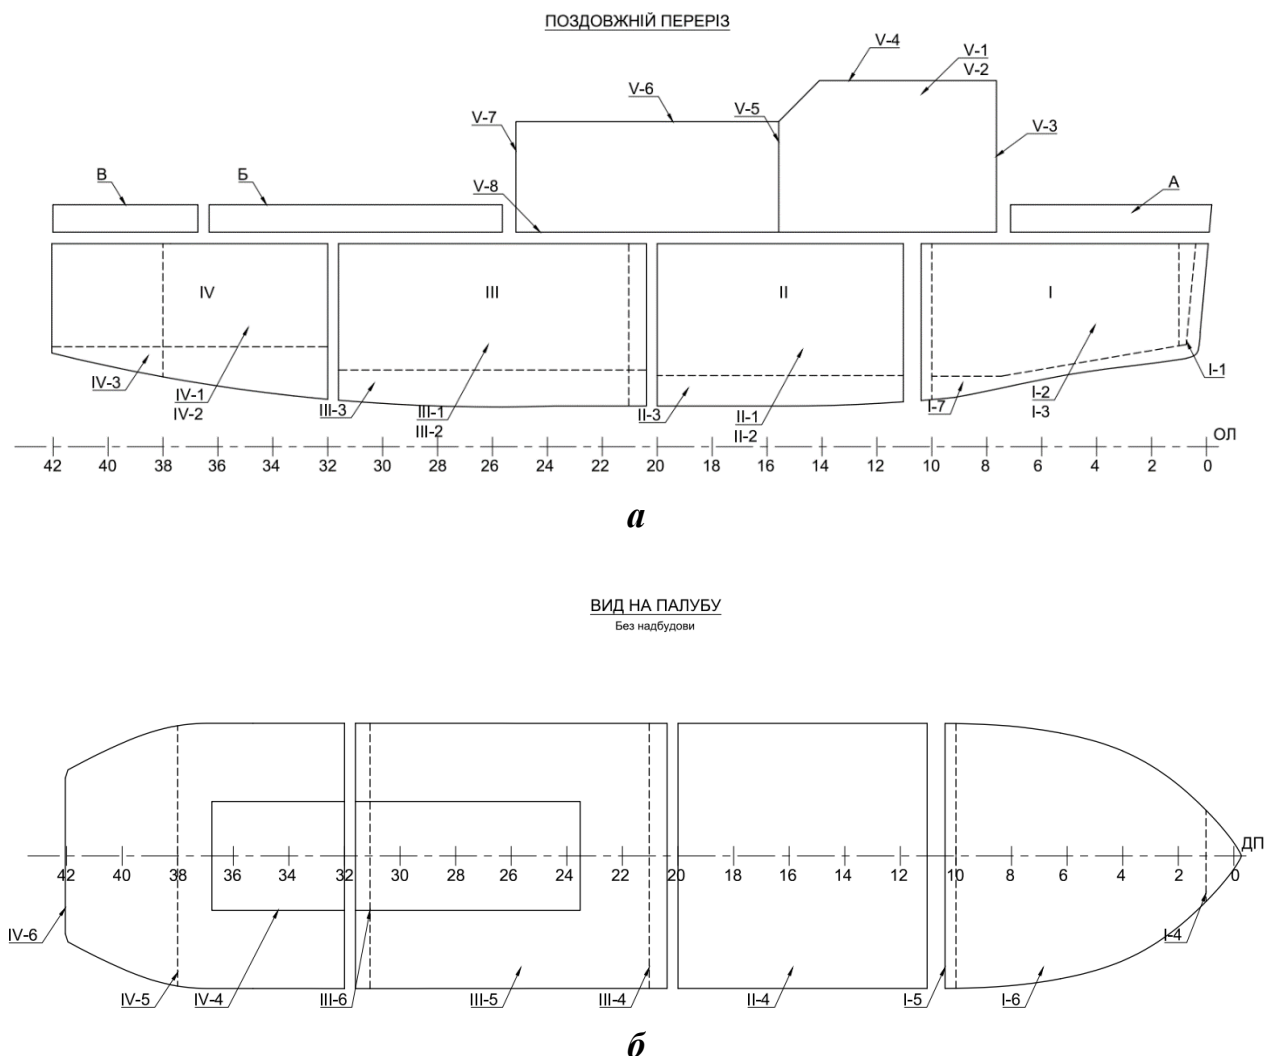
Розбивка корпусу катера на монтажні блоки:
